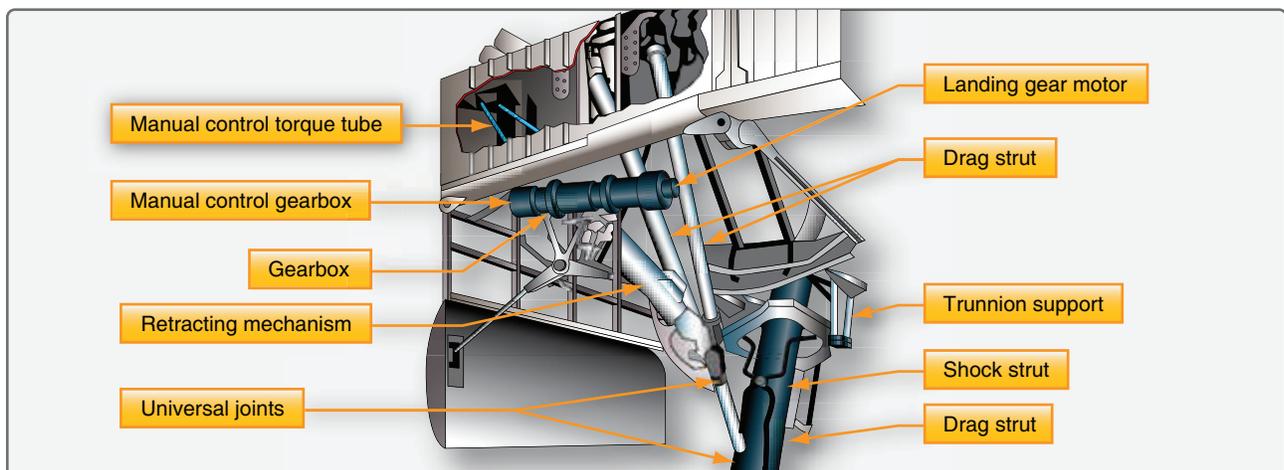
Sistema de retração de trem de pouso movido a motor elétrico.
